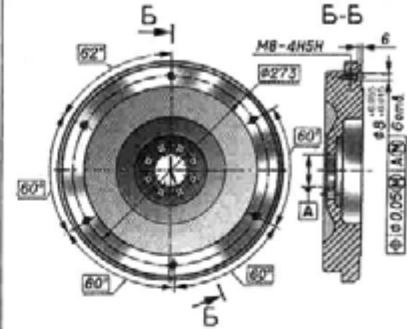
Расположение крепежных отверстий ведущего диска сцепления диафрагменного типа на маховике
